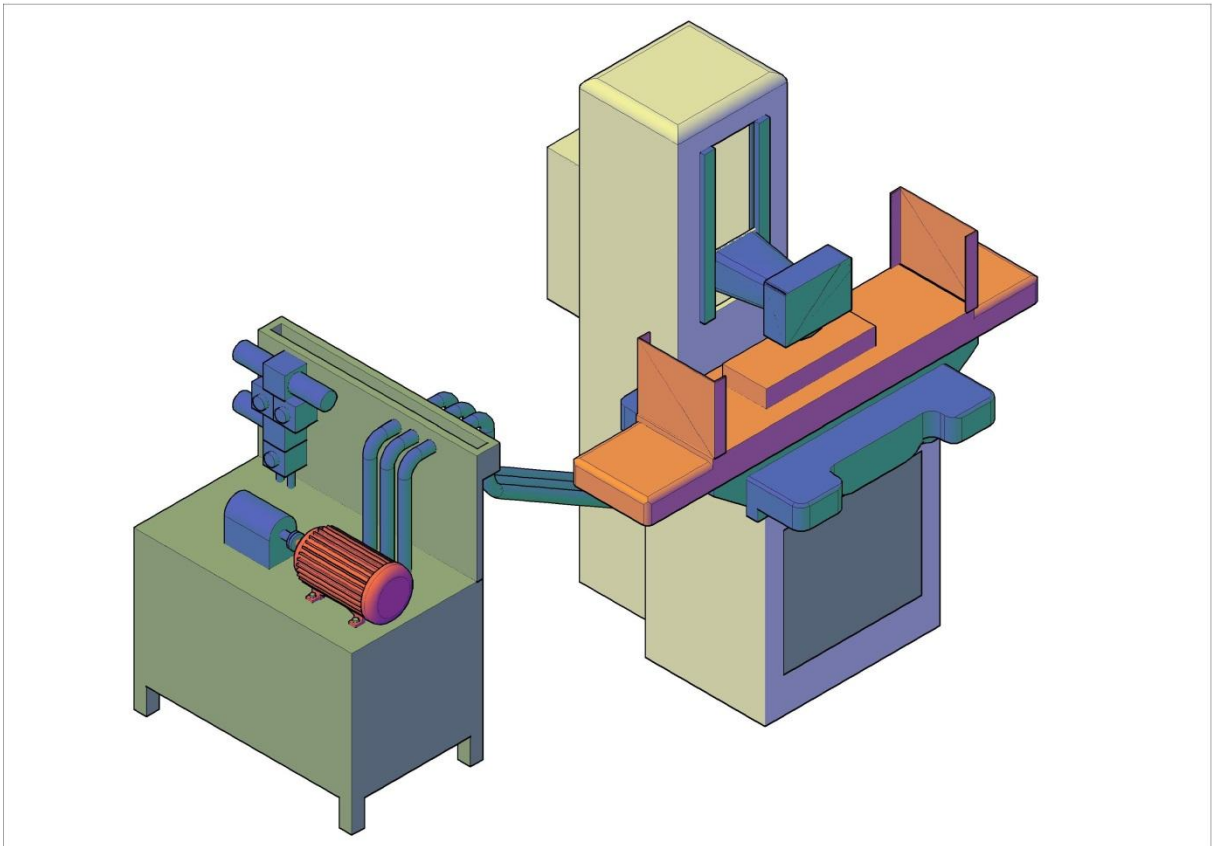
Desenho em 3dimensões Auto Cad 2013.
